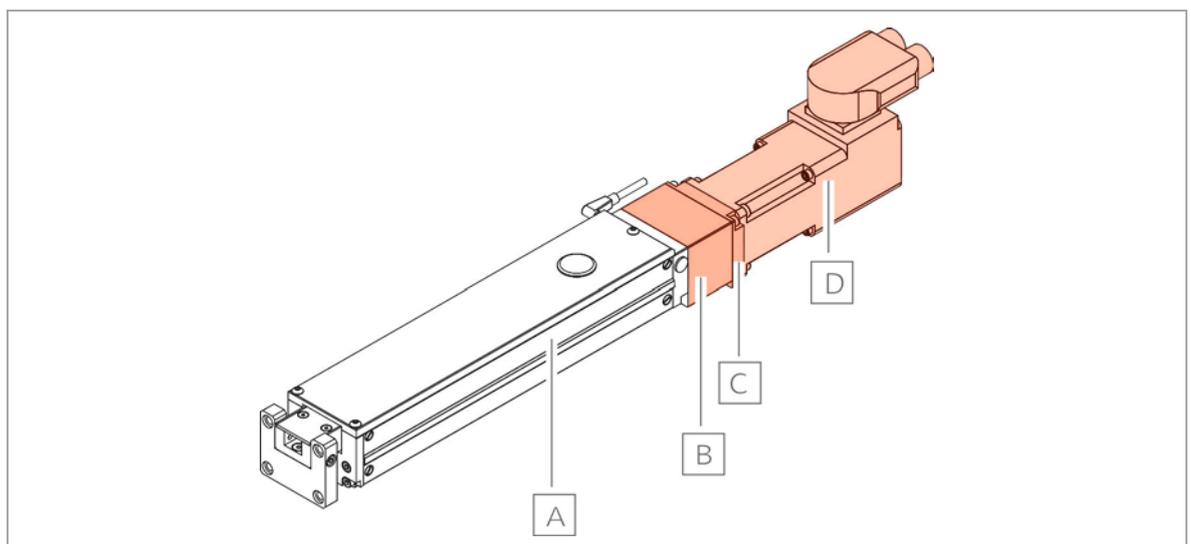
profiLINE 50 AL mit axialem Motoranbau
